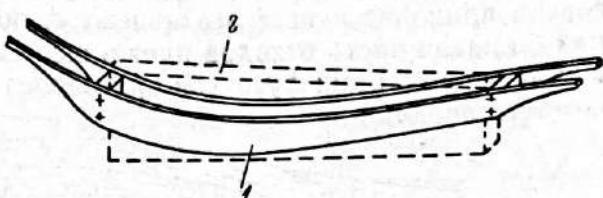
Копир-шаблон (цулага) для фрезерования футоксов.
